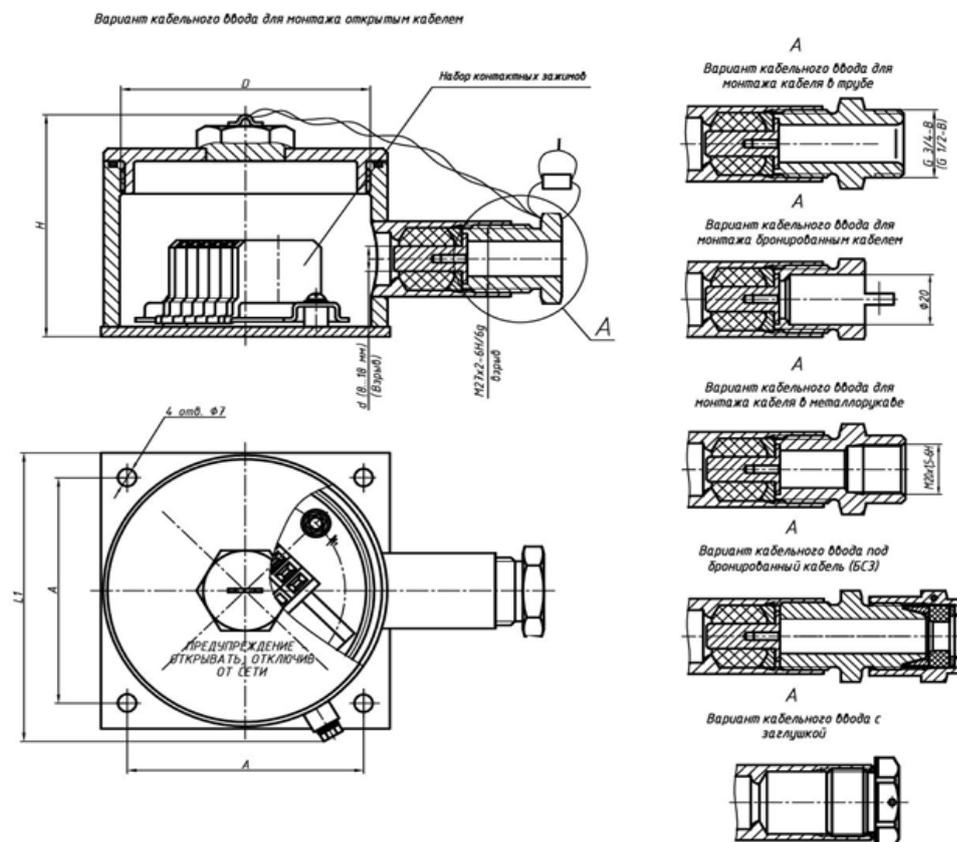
Габаритные, установочные и присоединительные размеры коробок ExКСУВ типа 1.
